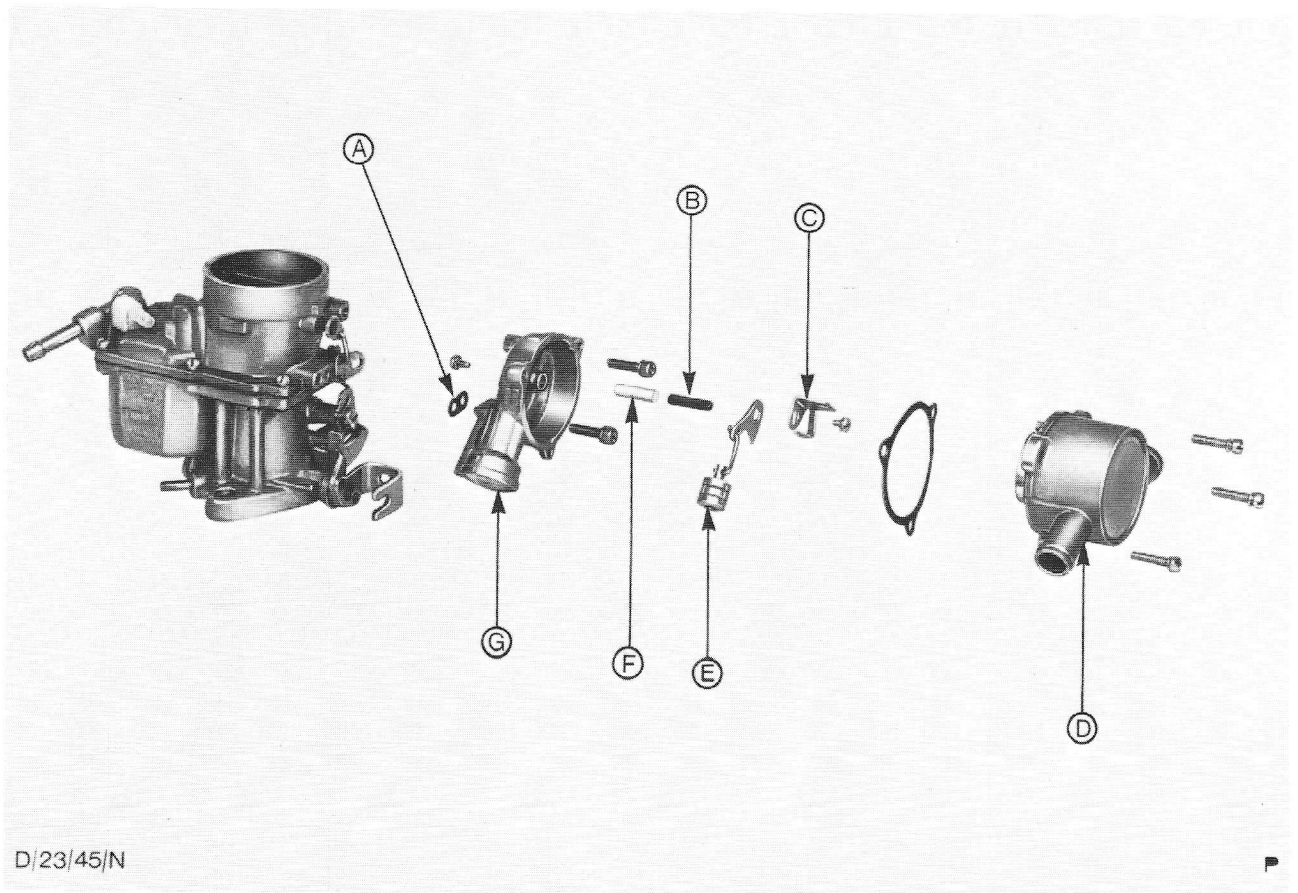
Bevestigingsbouten chokehuis aan carburateur
